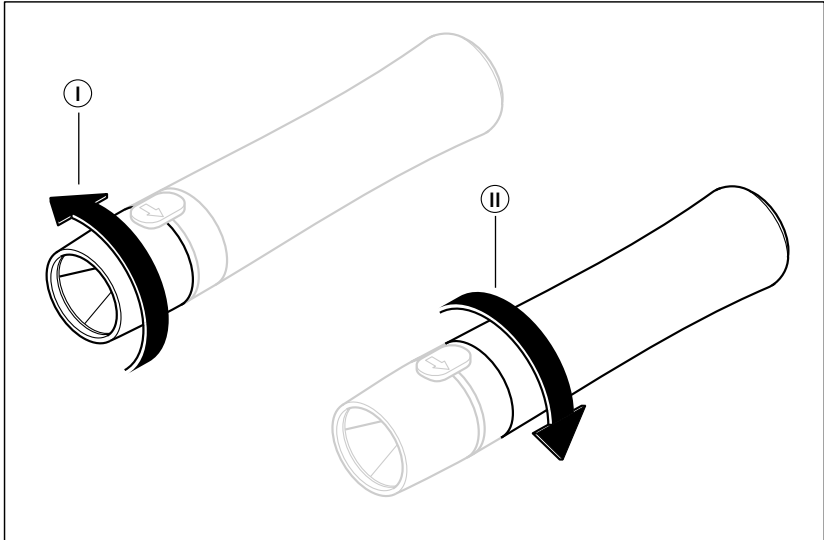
OPENING THE FRONT AND REAR HOUSING
